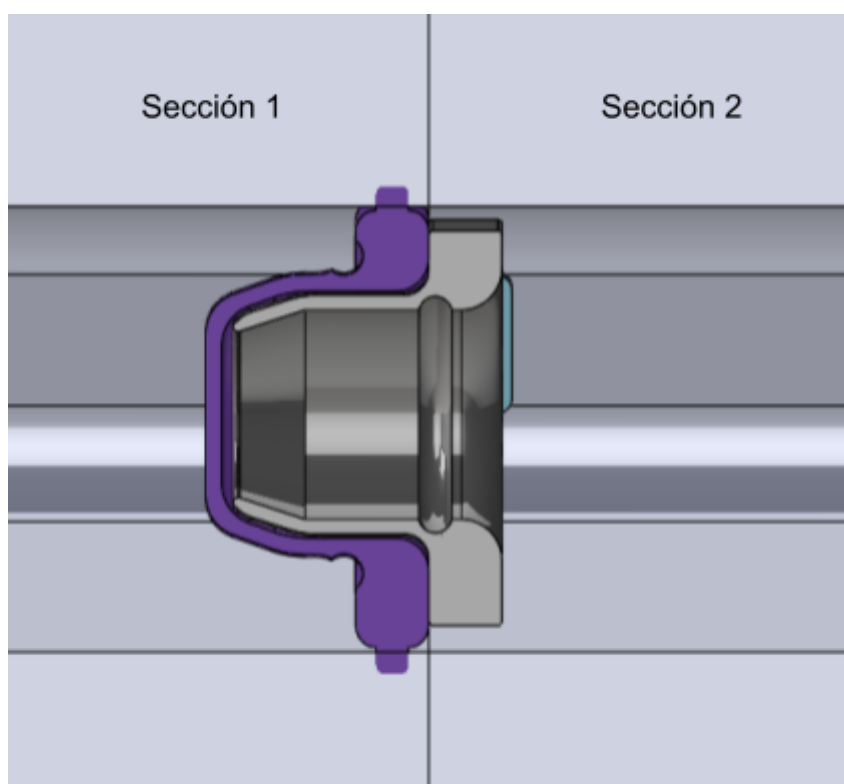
Vista sección de las piezas de unión dentro el agujero entre dos secciones de concreto. La pieza hembra es la pieza violeta en la izquierda, y la pieza gris en la derecha es la pieza macho.
